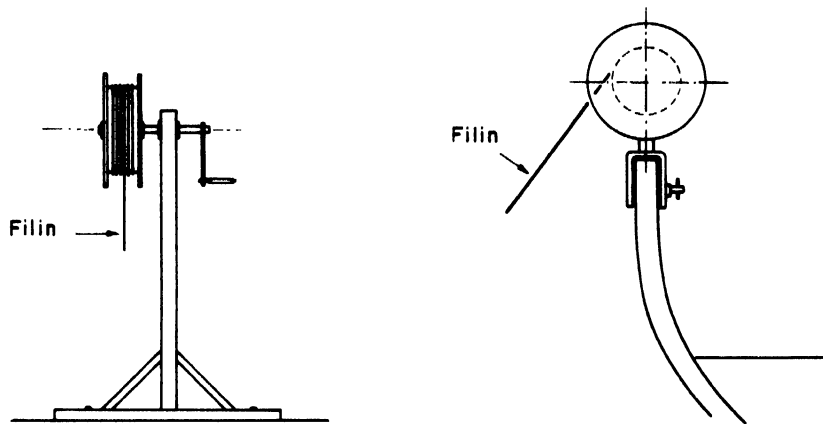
DETAILS DE CONSTRUCTION D'UN ENGIN DE LEVAGE SIMPLE
